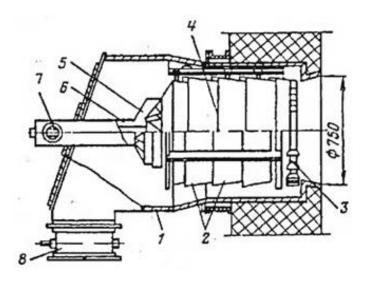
Схема предкамерной газомазутной горелки «Союзтехэнерго»: 1 — корпус; 2 — обечайки; 3 — сопла; 4 — щели; 5 — лопатки; 6 — коллектор; 7 — мазутная форсунка; 8 — шибер
